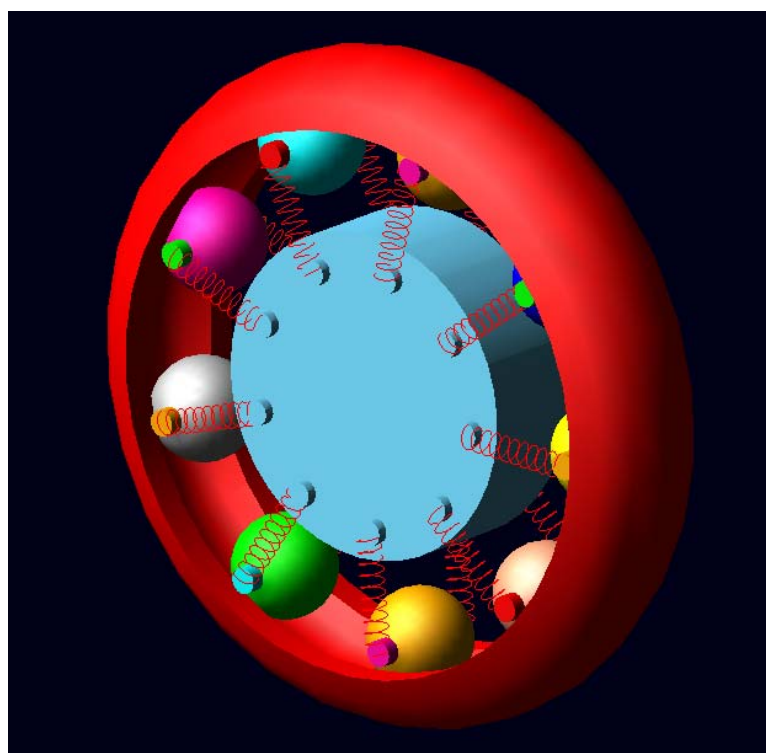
Vista isométrica del rodamiento de 9 bolas
